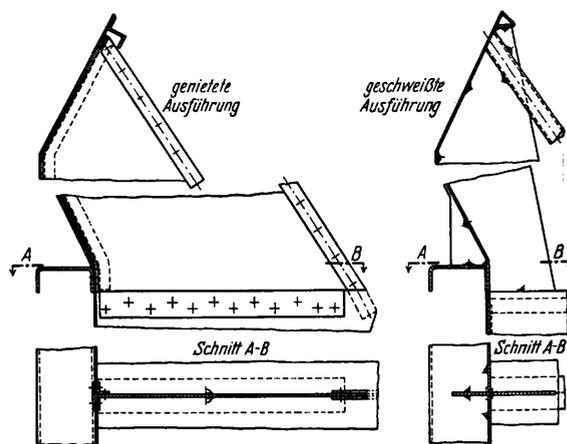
Stirnwandversteifung in genieteter und geschweißter Ausführung.
